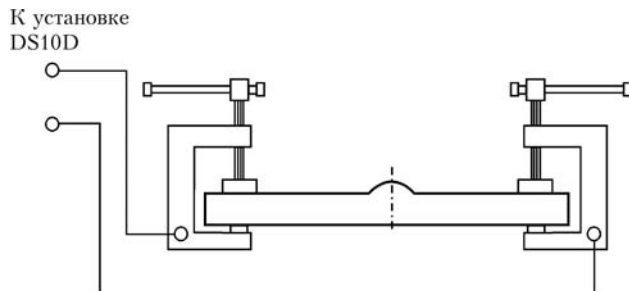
Схема подключения образца к установке при проведении ЭФО металла сварных соединений
